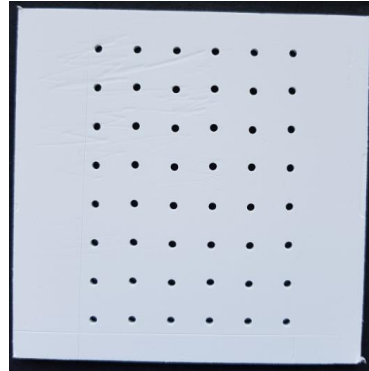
Foto de placa (90 mm X 90 mm) de furos de 2 mm
